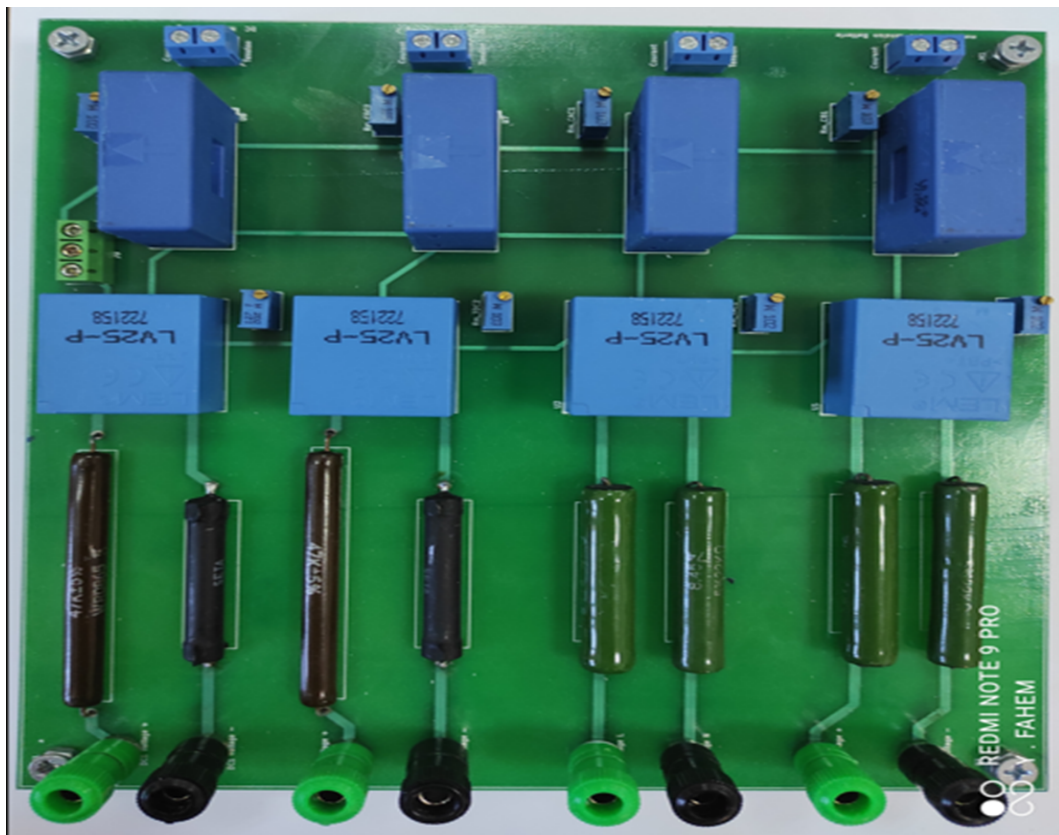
Vue de la carte secondaire mesure des paramètres électriques finie dimension 177x200 mm
